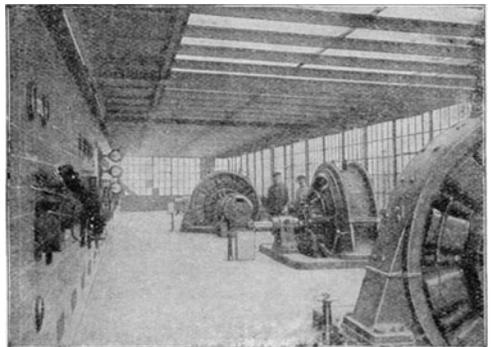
Schalttafel und Maschinenraum des Dreigruppenwalzwerkes.
